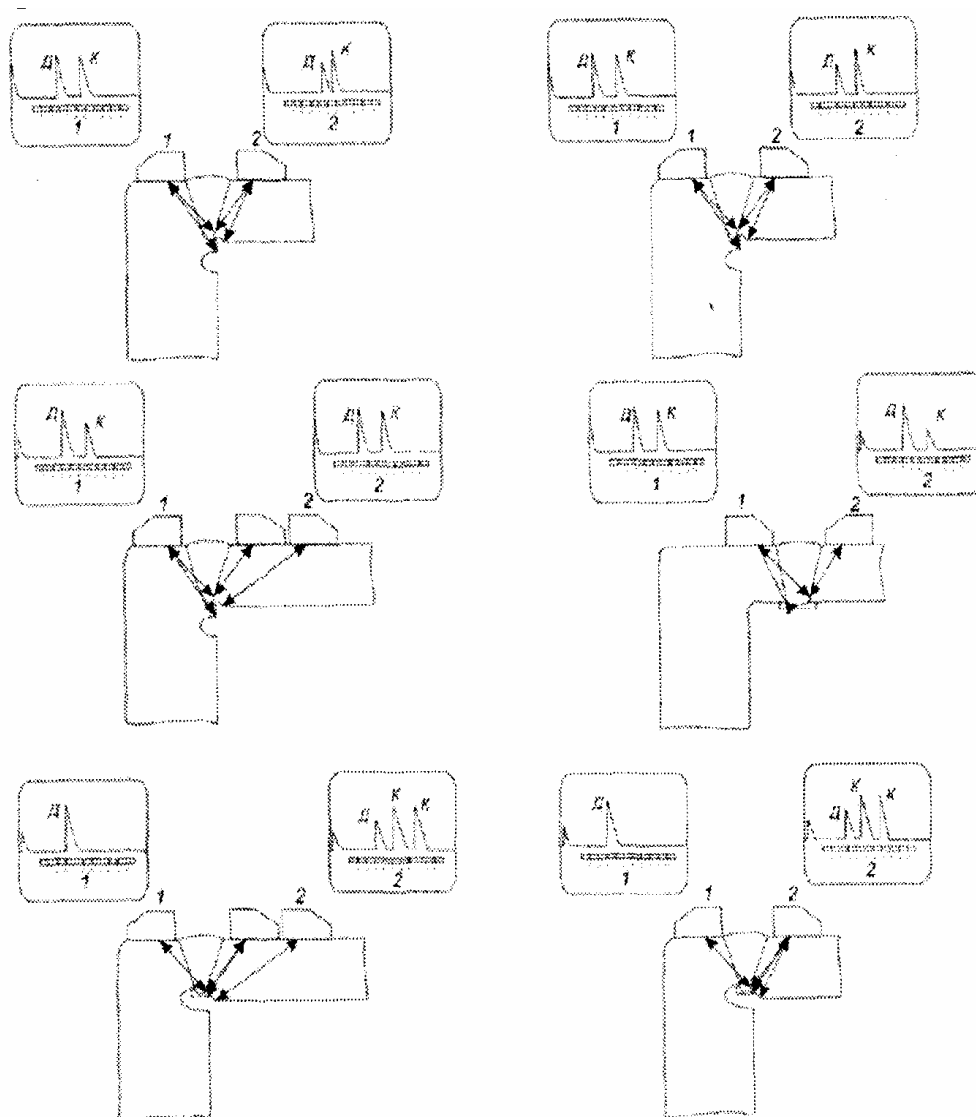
Схемы выявления корневых несуцільностей при контроле сварных соединений приварки доньшек покатыми преобразователями
